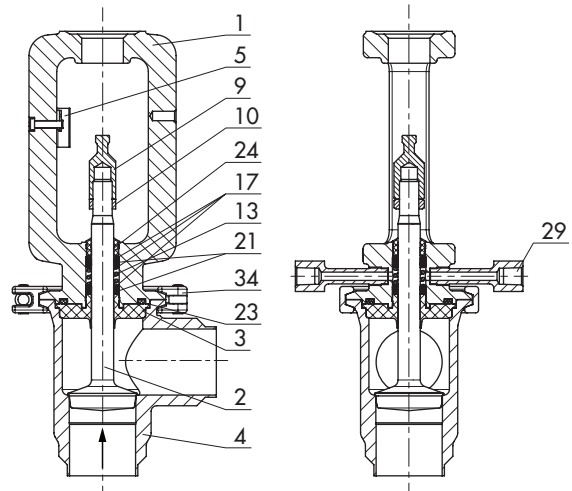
Ventil Typ 3347 zur Kombination mit Antrieb Typ 3271, Gussgehäuse mit Dampfsperre
